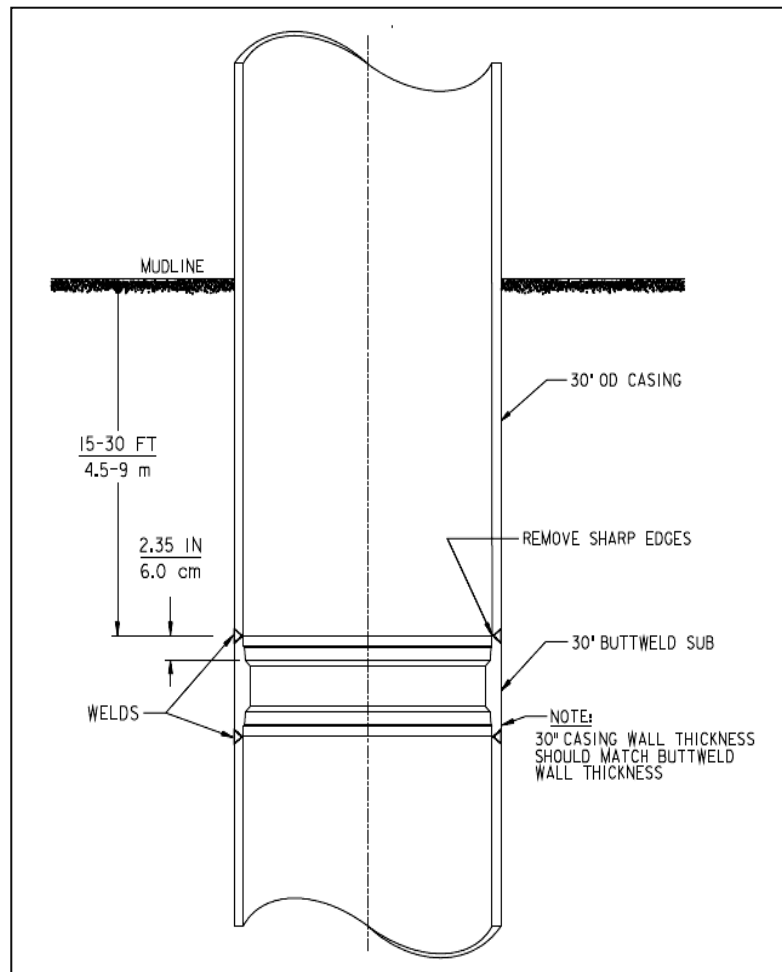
Conductor avec Butt-weld Sub installer.
